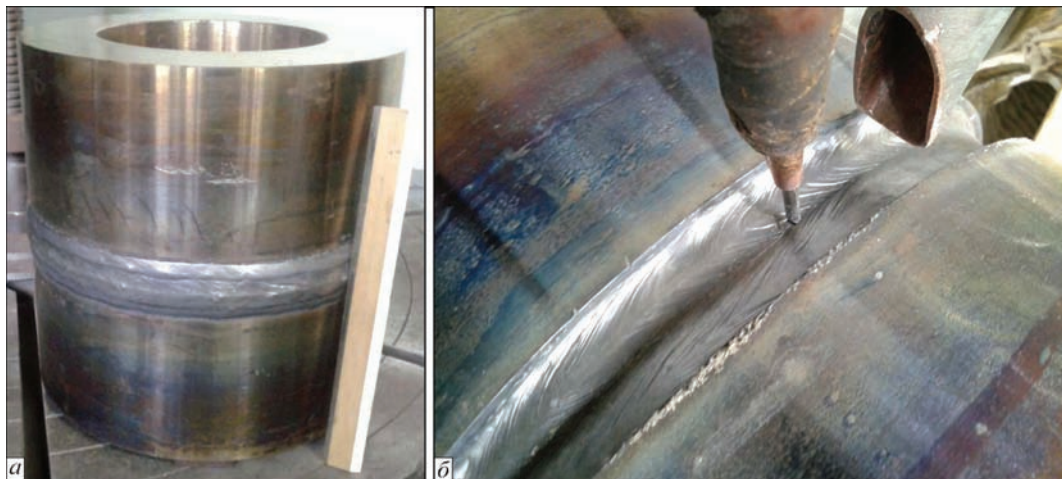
Сварное многопроходное кольцевое соединение (а — сварной образец, б — сварка кольцевого шва)
